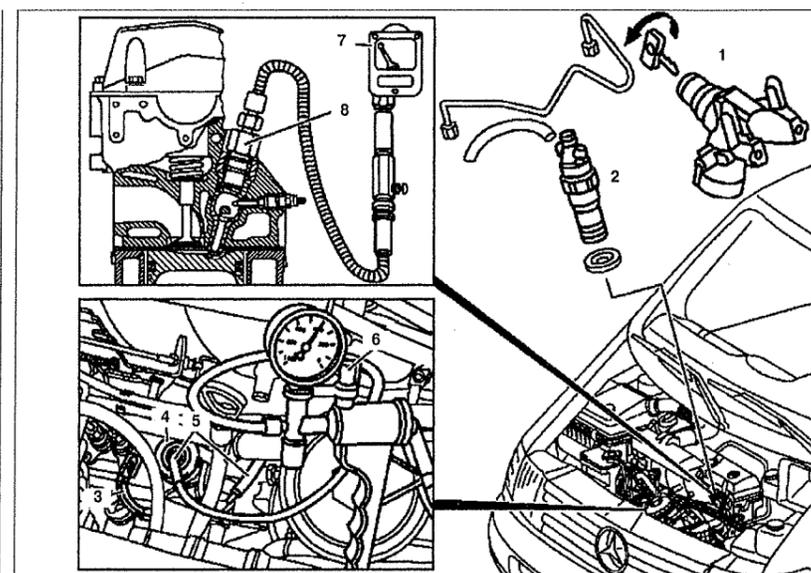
Проверка компрессии двигателя: 1. Выключатель зажигания, 2. Форсунка, 3. Упорный рычаг, 4. Стопорная вакуумная капсула, 6. Ручной вакуумный насос, 7. Компрессометр, 8. Соединитель.
